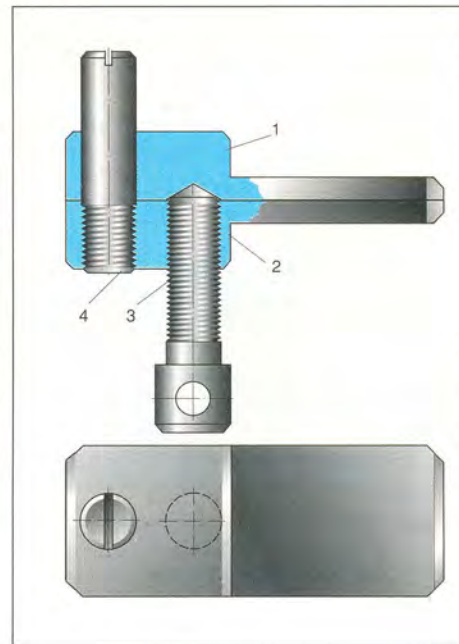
Приспособление для “разрабатывания” поршней без винта с левой резьбой: 1, 2 – лапки; 3 – винт; 4 – направляющий палец.
